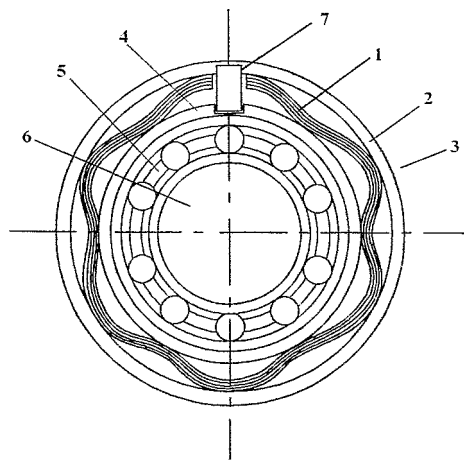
Внешний вид демпфера с саморазгрузкой от веса ротора [3]
